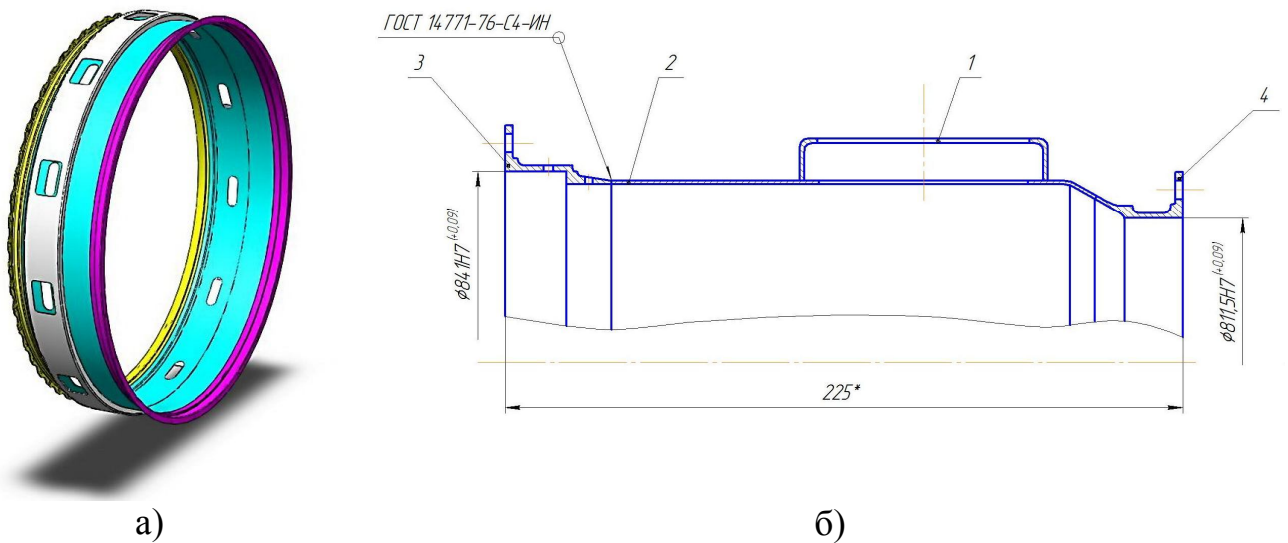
Корпус ТНД (а) и его поперечное сечение с указанием рассматриваемого сварного шва (б)
